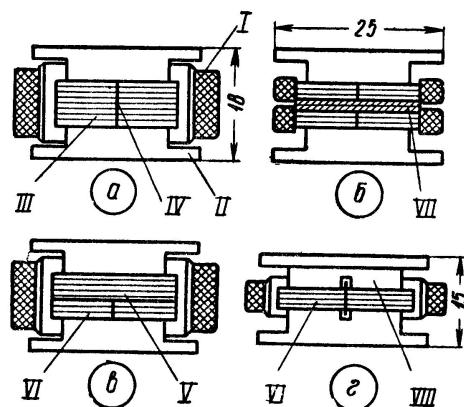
Магнитные головки для однодорожечного и двухдорожечного магнитофонов
